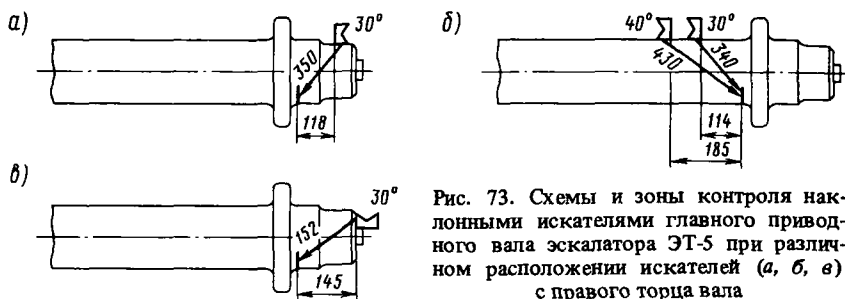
Схемы и зоны контроля наклонными искателями главного приводного вала эскалатора ЭТ-5 при различном расположении искателей (а, б, в) с правого торца вала
